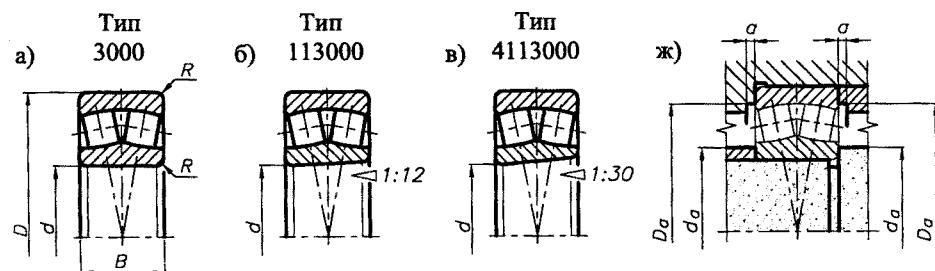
Габаритные и установочные размеры радиальных роликовых сферических двухрядных подшипников
